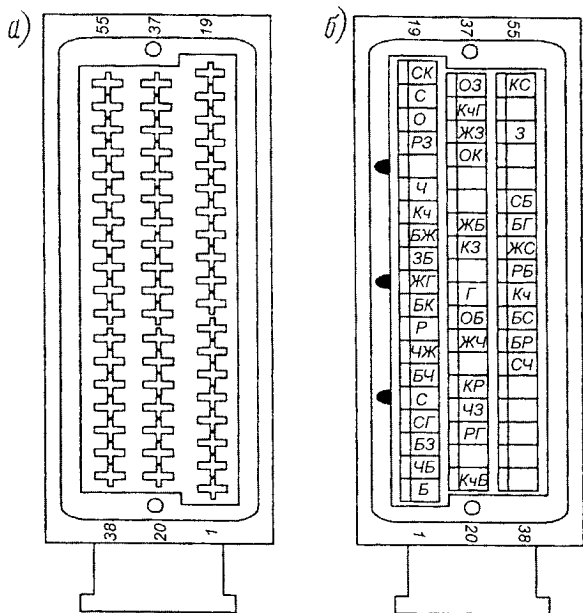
Схема розетки 55-контактного соединителя блока управления:
